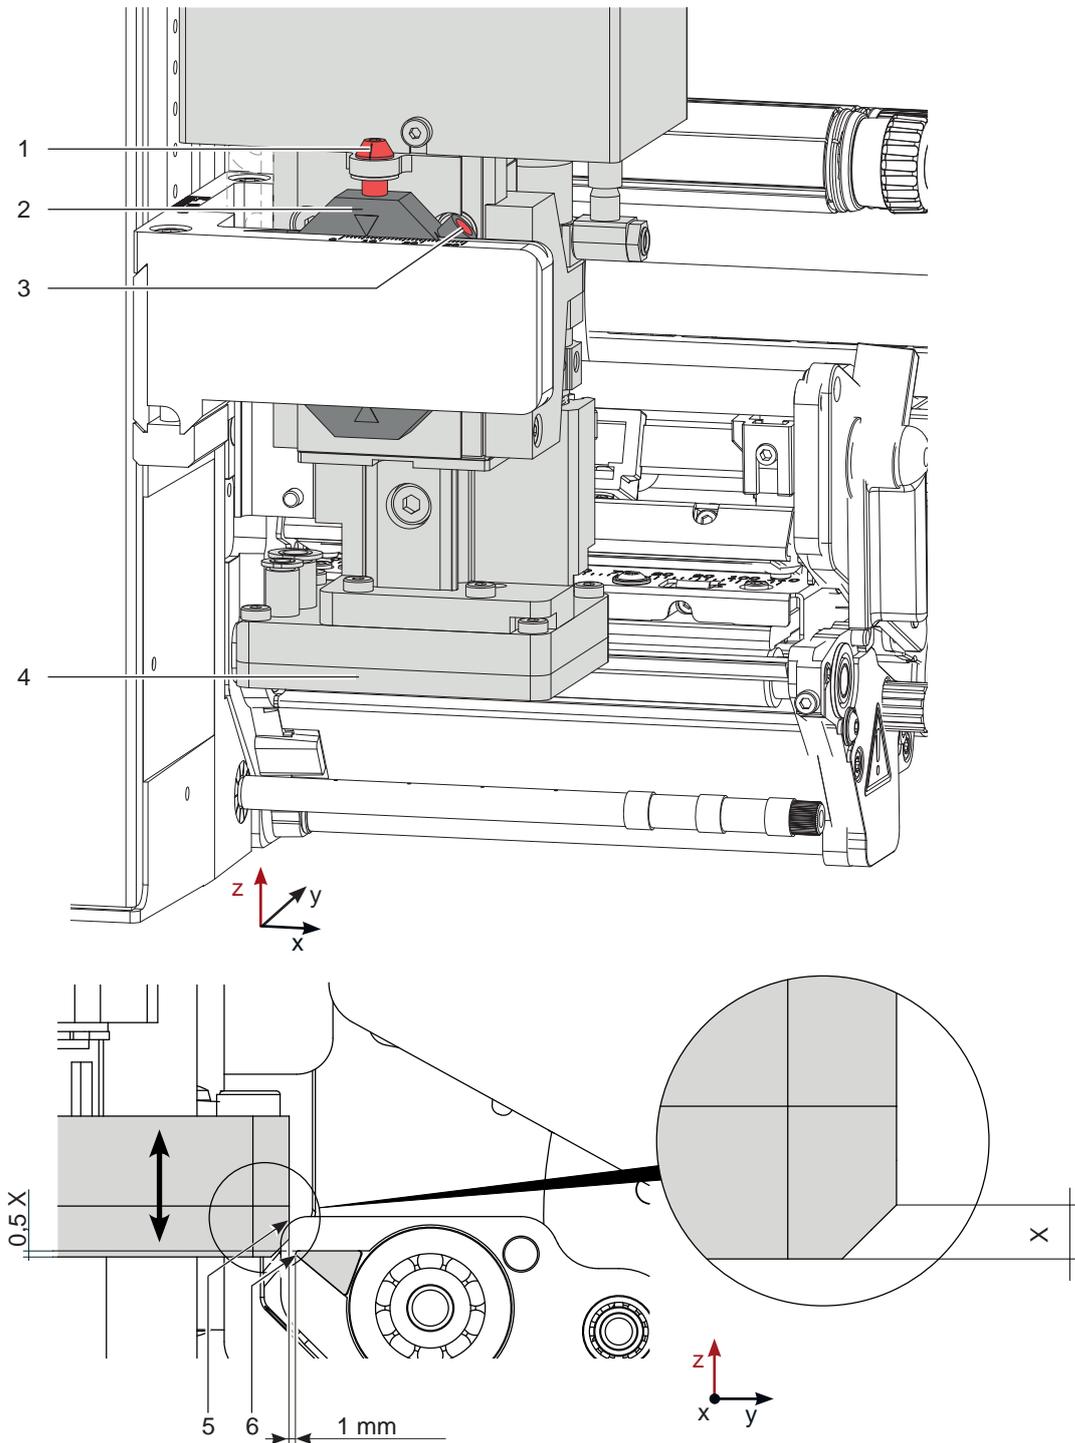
Verschiebung der Stempelbaugruppe in Z-Richtung
